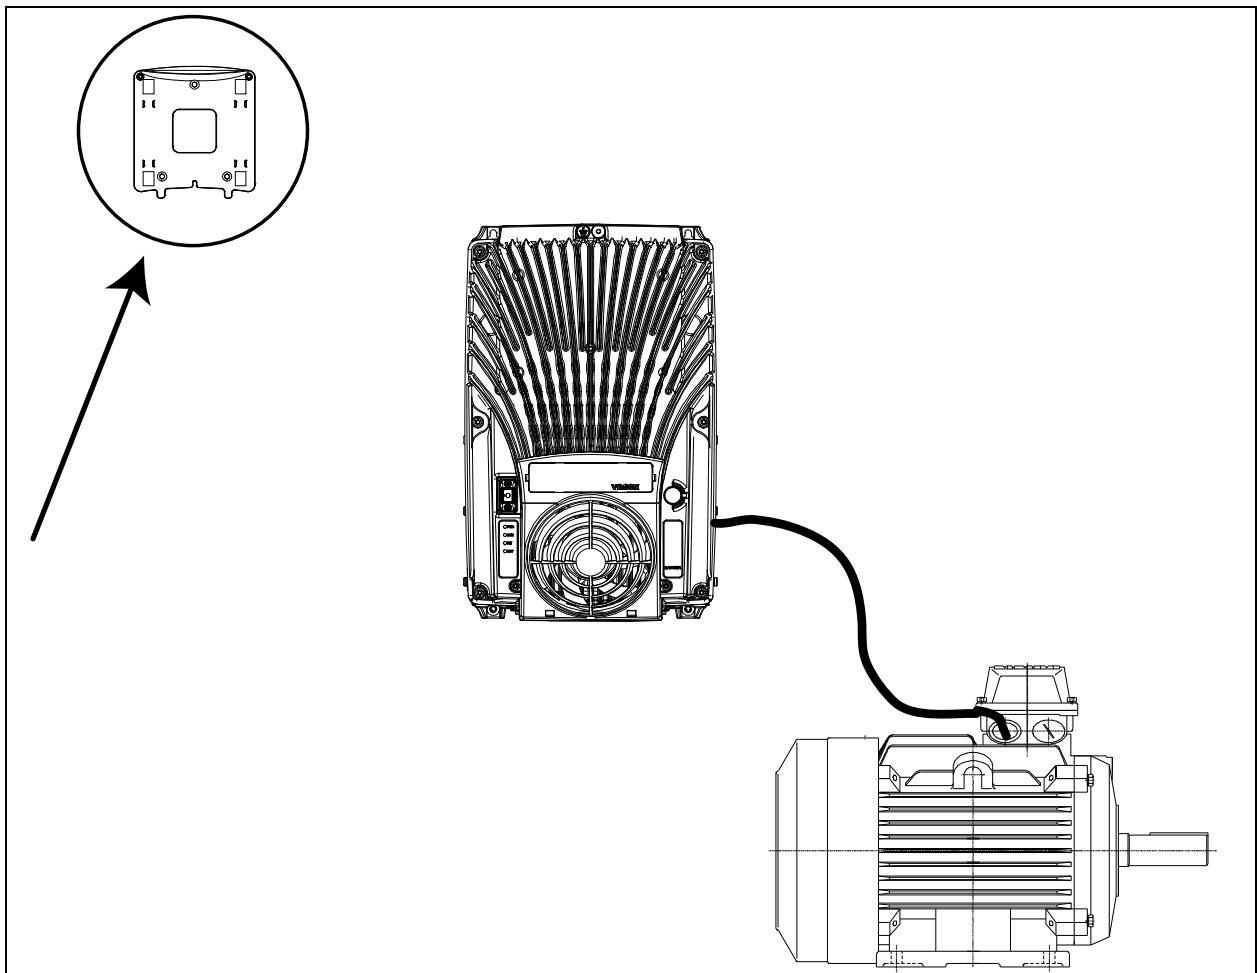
Fissare il supporto del pannello su una parete o nella posizione più favorevole.
